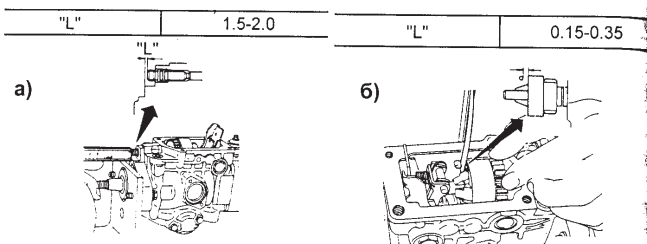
Регулировки установочных размеров «L»: вала регулятора (а) и осевого зазора держателя грузов (б).
